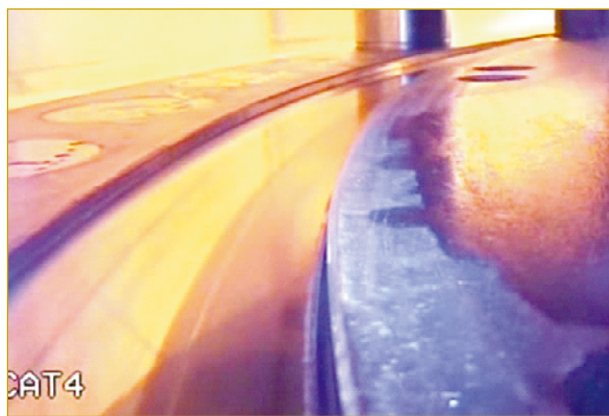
Visión desde el ROS Flangebot durante una inspección.
